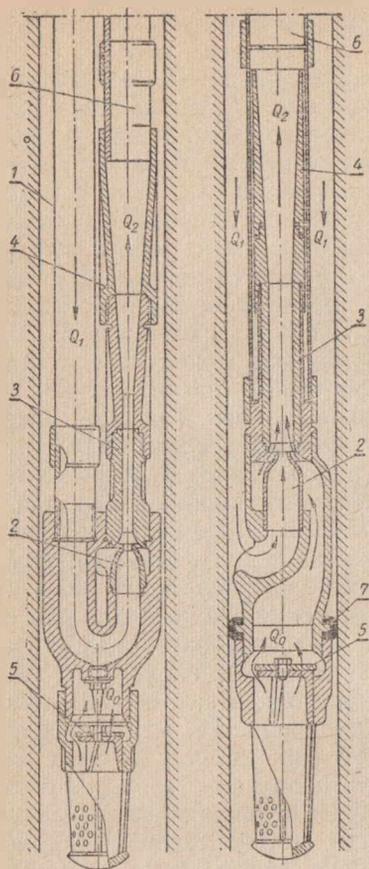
Конструкции двух- (слева) и однолинейного струйных аппаратов:
